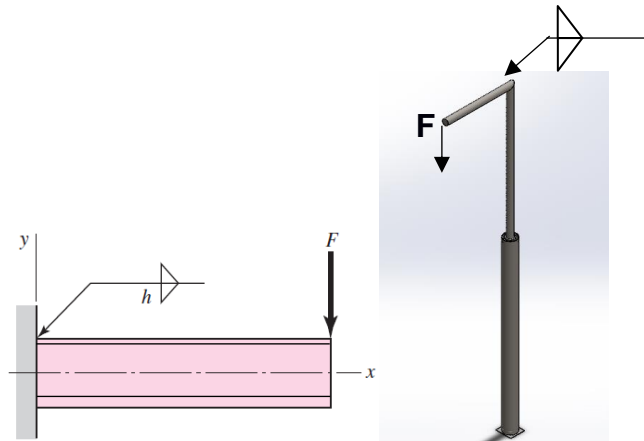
Voladizo de sección circular soldada a un soporte
